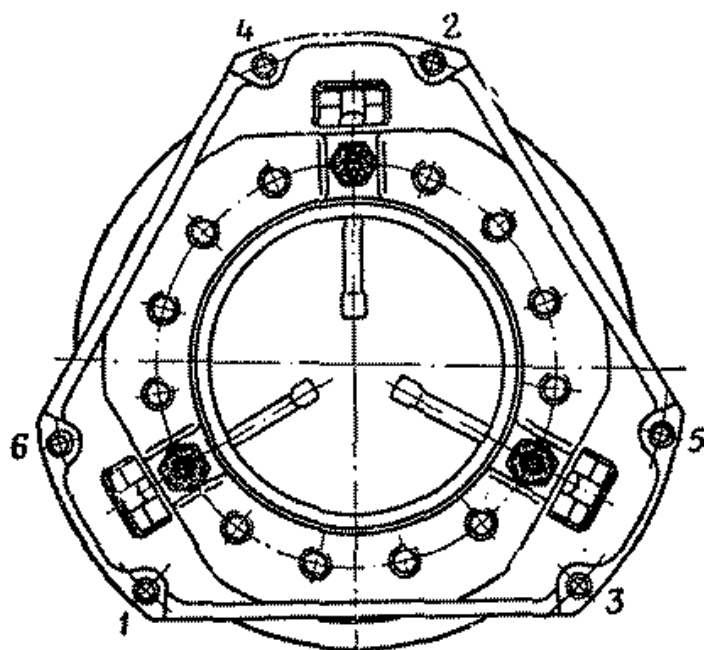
Порядок затяжки болтов крепления кожуха сцепления к маховику двигателя
